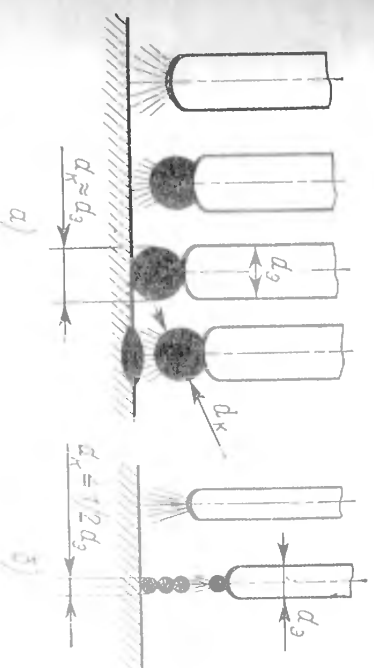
Схемы крупнокапельного (а) и струйного (б) переноса электрода на заготовку при короткой дуге:
